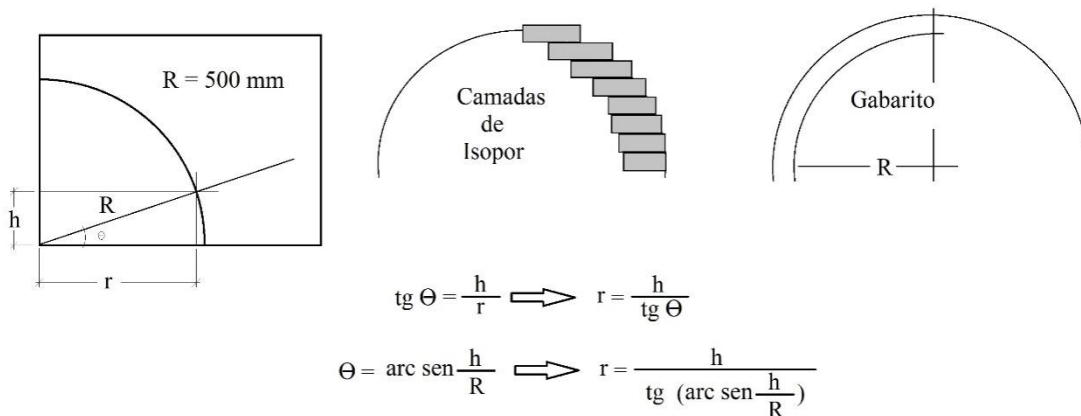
Esquema e equações usadas para se calcular as dimensões das camadas de isopor para construir o molde.
